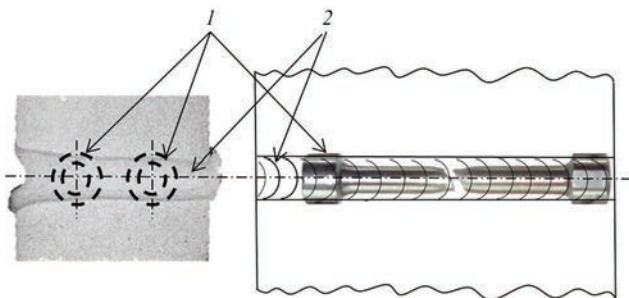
Схема вирізки зразків для випробувань на розтяг металу зварного шва: 1 — зразки; 2 — зварний шов
